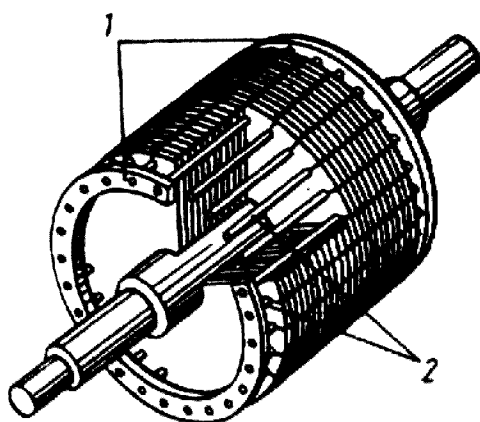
Короткозамкнутый ротор асинхронного двигателя со сварной обмоткой: 1 — замыкающие кольца; 2 — стержни обмотки
